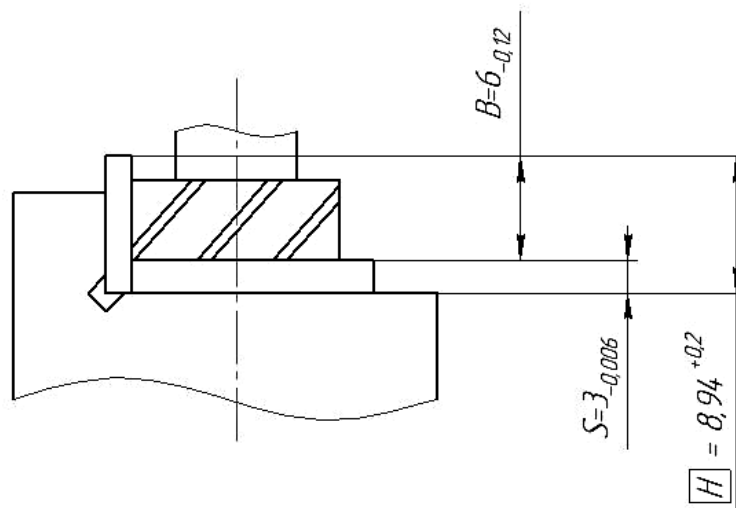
Схема налаштування інструмента для фрезерування уступа
